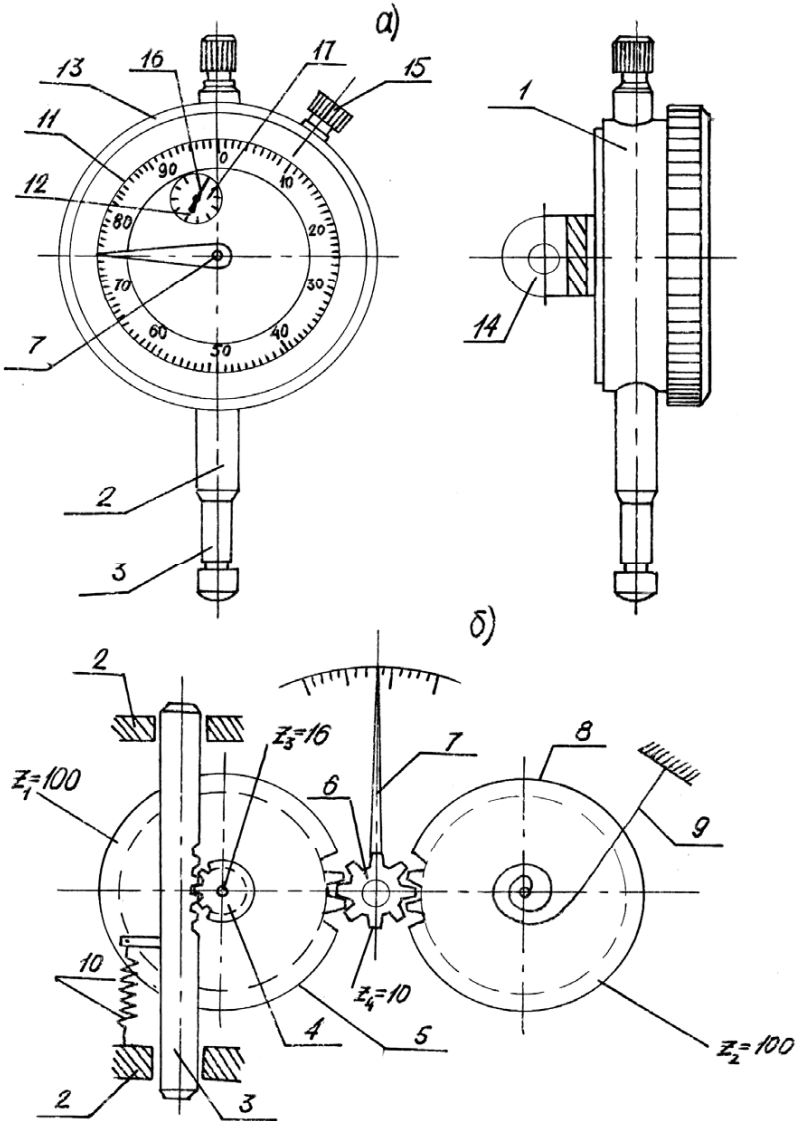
Індикатор годинникового типу: *а* – загальний вигляд; *б* – зубчата передача
